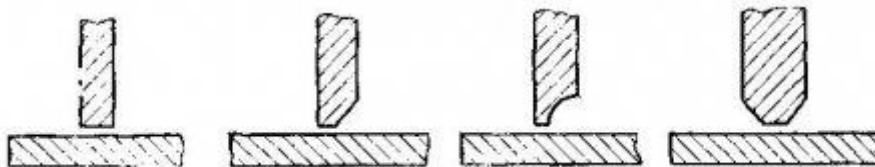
Форма подготовленных кромок под сварку для тавровых соединений
